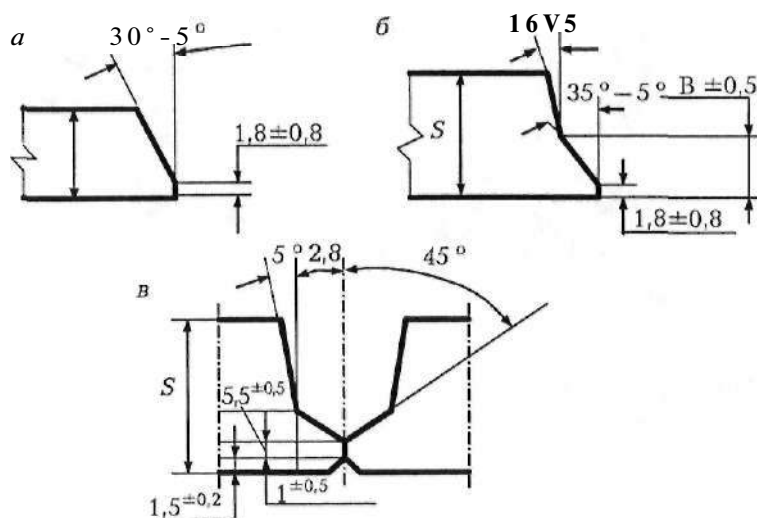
Типы разделки кромок труб для ручной дуговой сварки, односторонней автоматической сварки под флюсом, автоматической дуговой сварки порошковой проволокой с принудительным формированием, полуавтоматической сварки в защитных газах:
